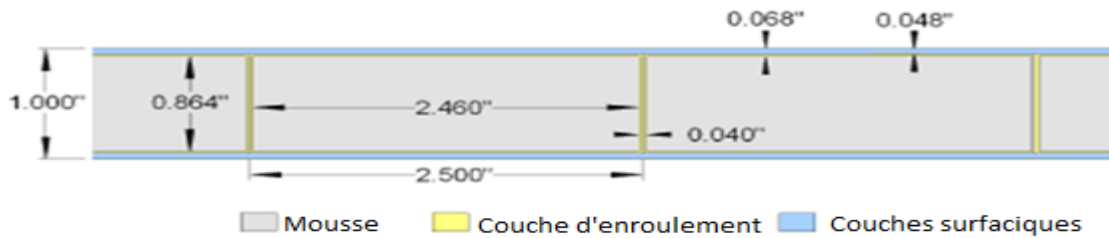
Représentation d'une coupe d'un sandwich (FRF ou RCS) (Source : [37] traduit)
